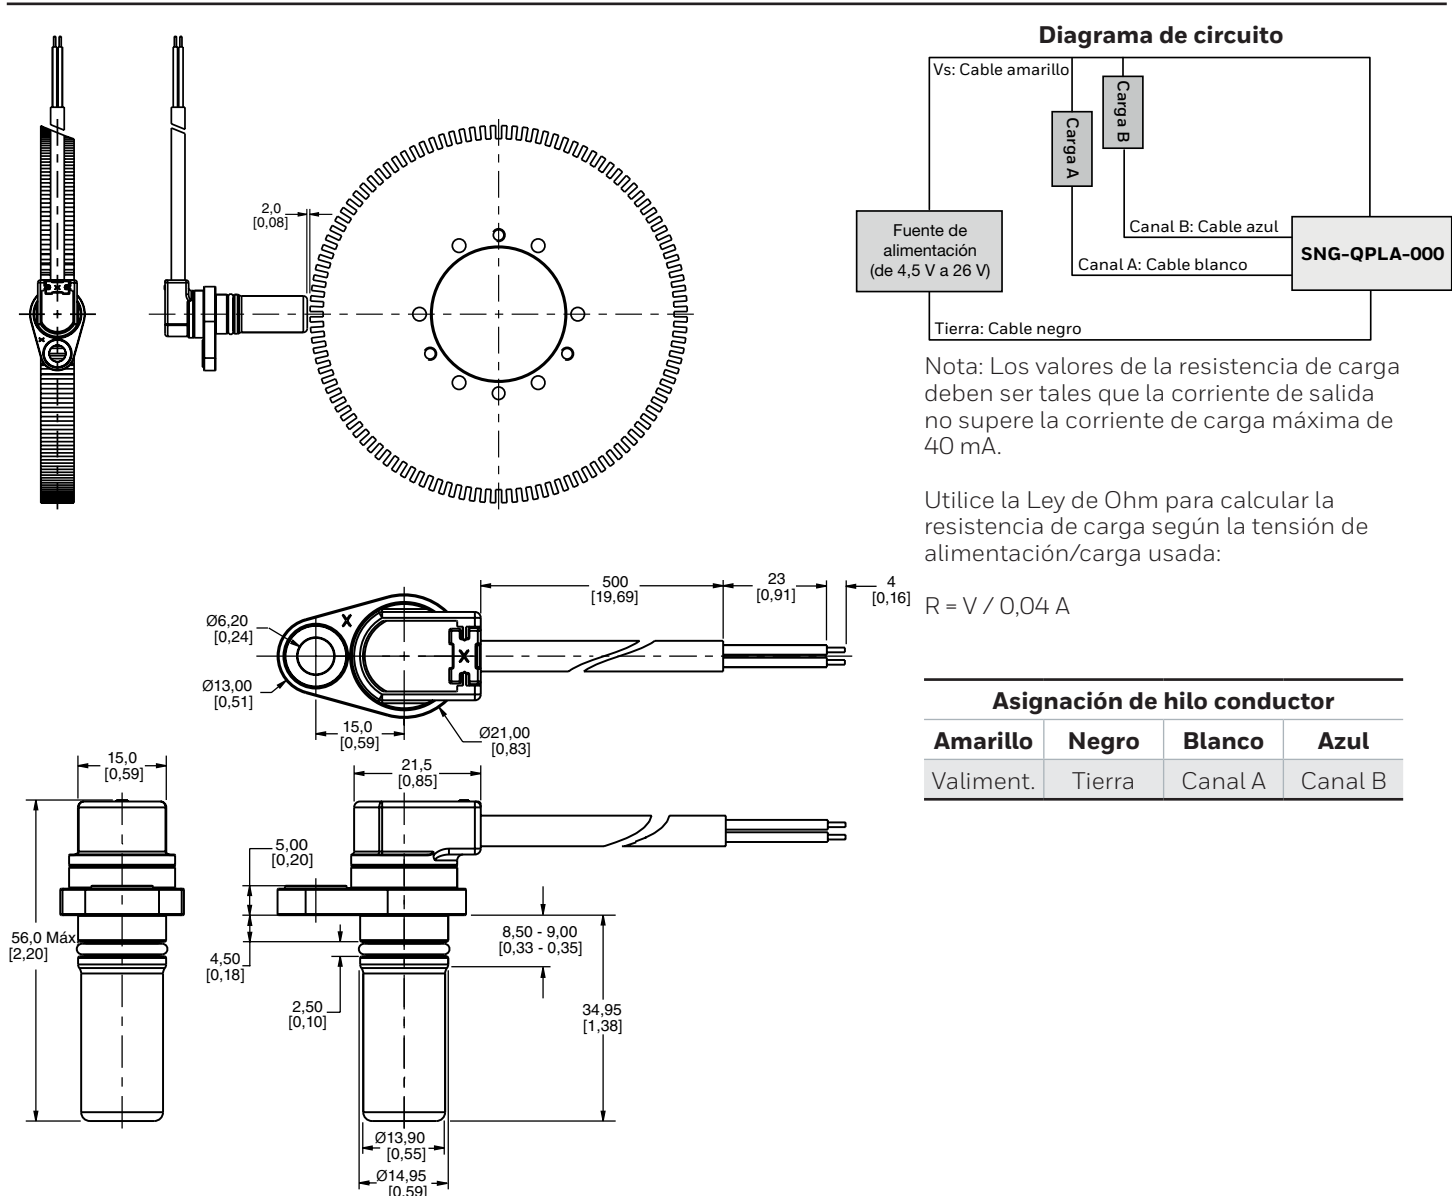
Dimensiones de montaje de SNG-QPLA-000 (solo para consulta: mm/[in])
